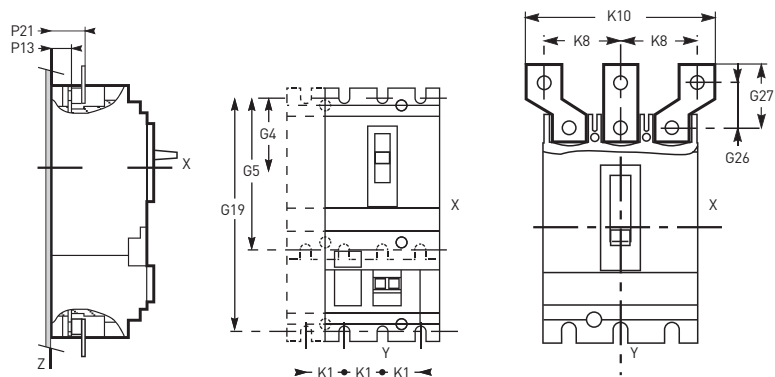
Присоединительные размеры автоматических выключателей BA-99C 100/160/250/400/630
